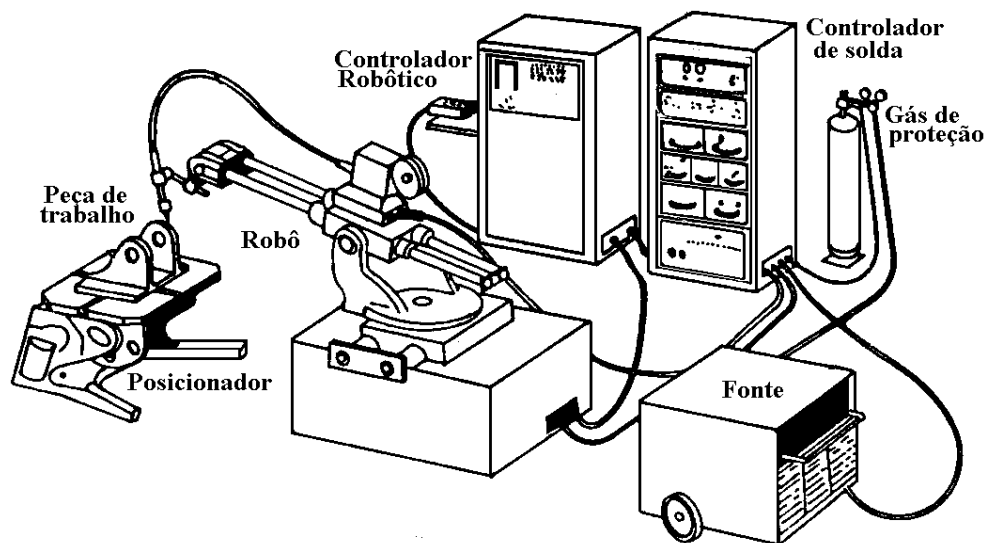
Esquema de montagem de robô industrial com solda MIG
